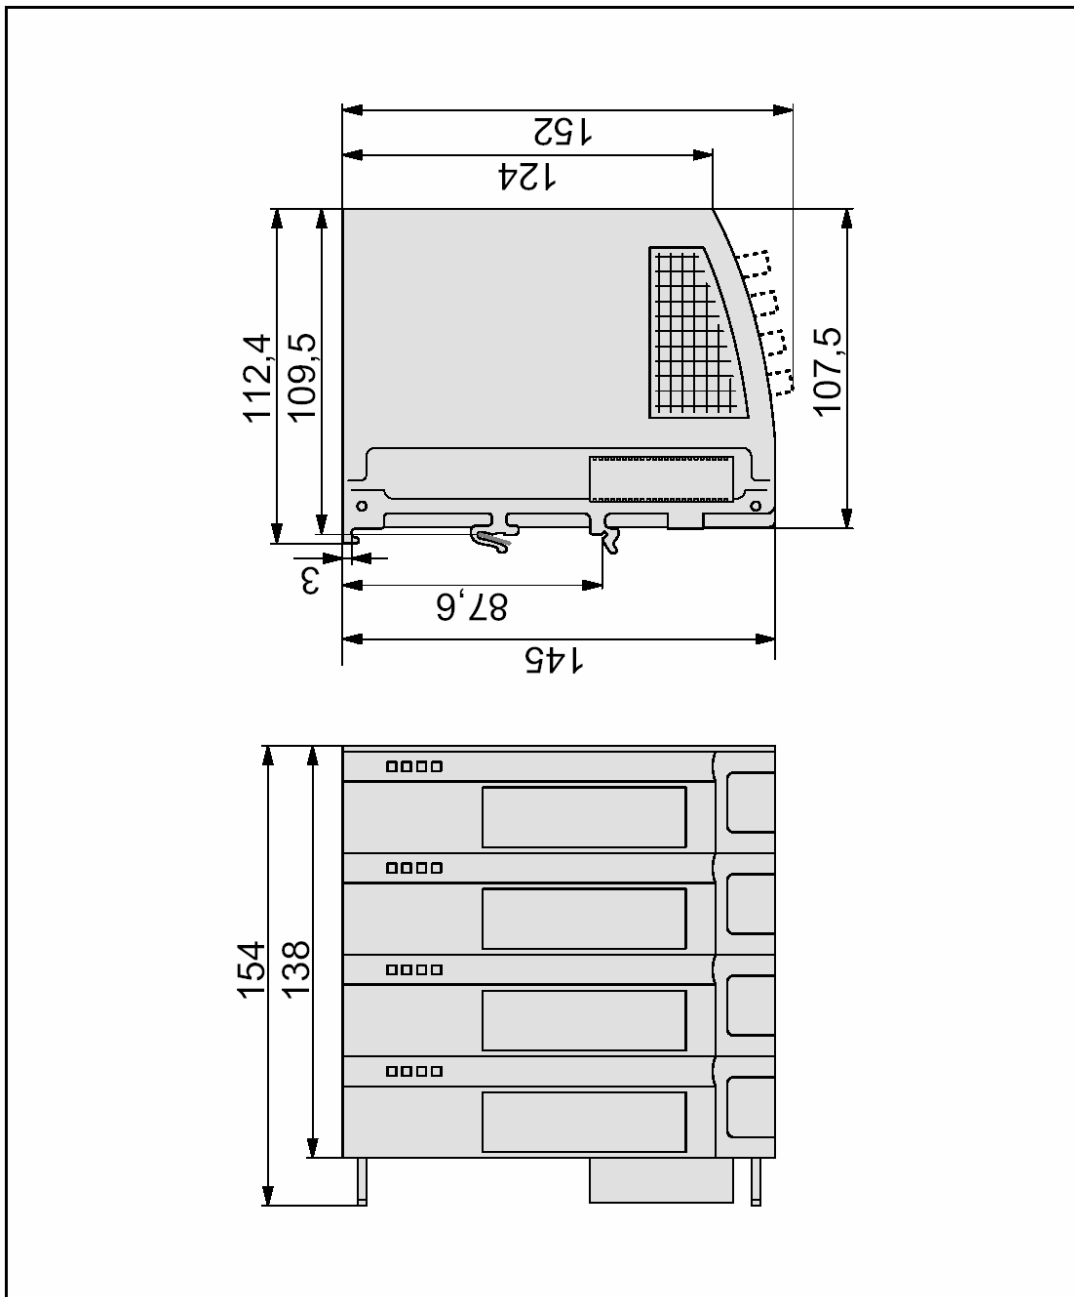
Габаритные размеры модуля расширения EM496-4
